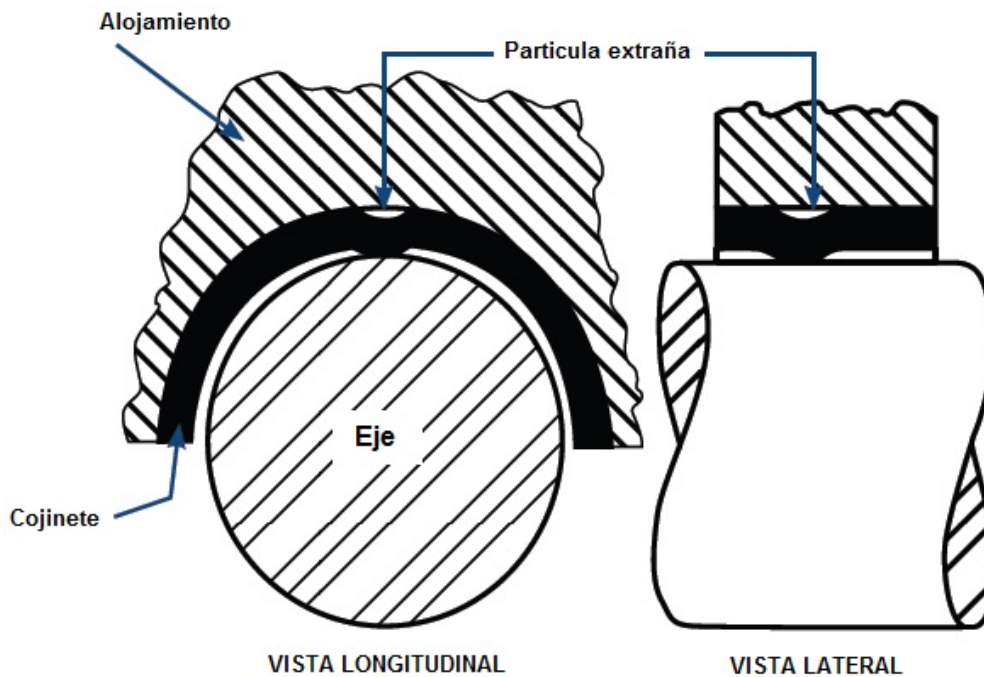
Vista del punto alto creado en el cojinete.
